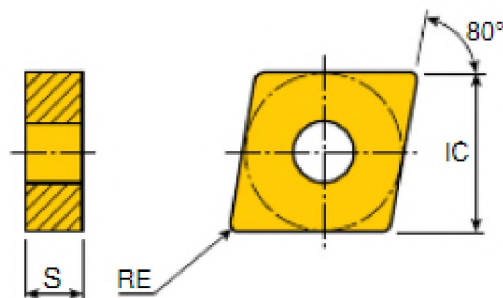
Пластина CNMG-090408EA .CVD покриття : TT5080
